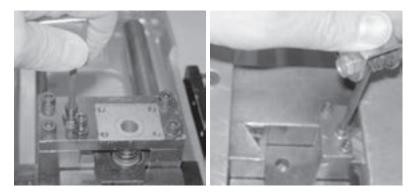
Pour alléger le serrage du plateau, desserrez les vis avant (à gauche) et serrez la vis arrière.
